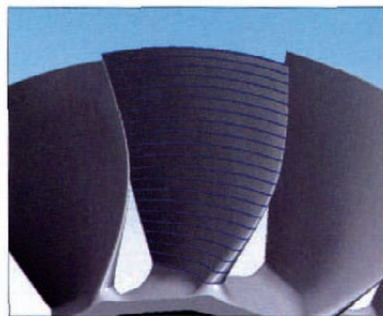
整体叶轮精加工等参数刀具轨迹和加工仿真图
